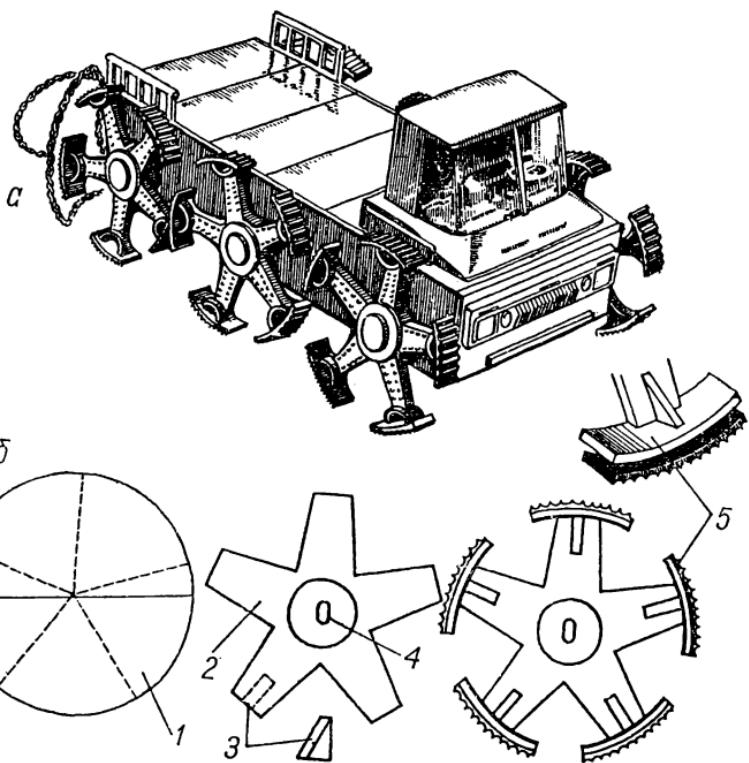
Внешний вид модели вездехода-шагохода (а) и технология изготовления шагающего колеса (б):
